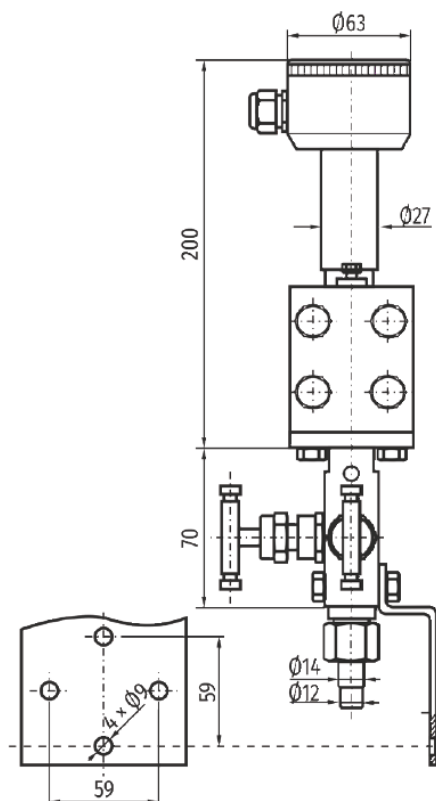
Крепление U и пример монтажа к плоской поверхности преобразователя PR-28 с типом процессного присоединения СН в комплекте с вентильным блоком
